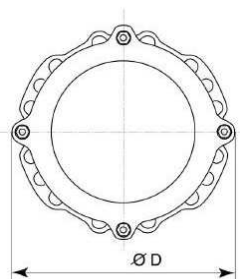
Saint Gobain Ultraquick: Vista frontal
